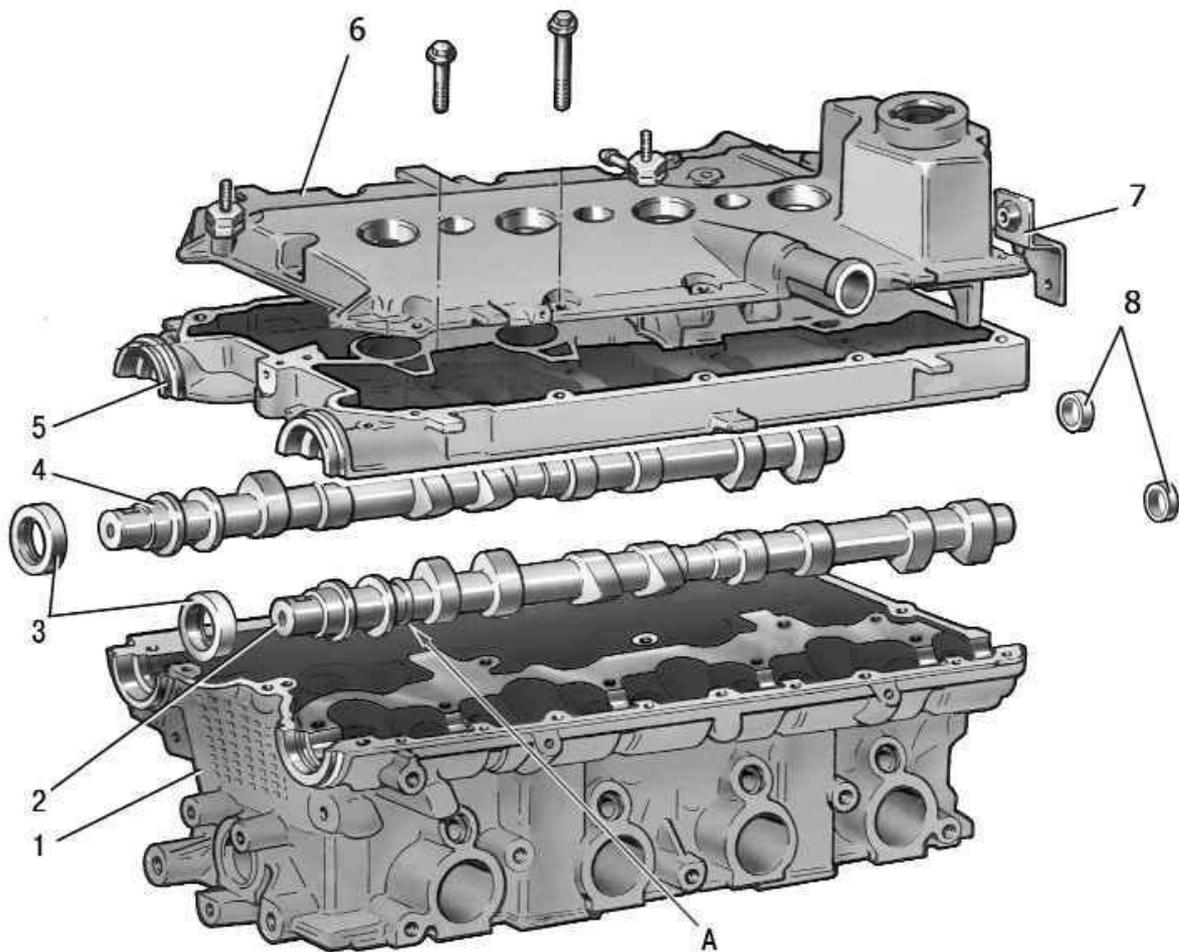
Детали головки блока цилиндров: 1 – головка блока; 2 – впускной распределительный вал; 3 – сальник; 4 – выпускной распределительный вал; 5 – корпус подшипников распределительных валов; 6 – крышка головки блока; 7 – кронштейн крепления жгута проводов; 8 – заглушки; А – отличительный поясok впускного распределительного вала.
